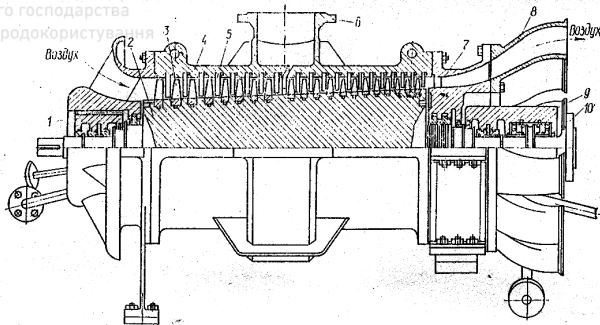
Осьовий турбокомпресор: 1- опорний підшипник; 2- барабан; 3- робоча лопатка напрямного апарату; 6- патрубок проміжного відбору; 7- дифузор; 8- перехідний патрубок; 9- опорно-упорний підшипник; 10- фланець жорсткої муфти
